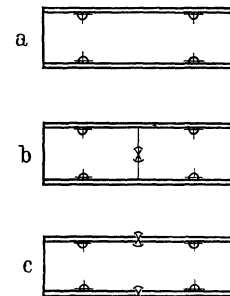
Grundformen des geschweißten Trägers.
